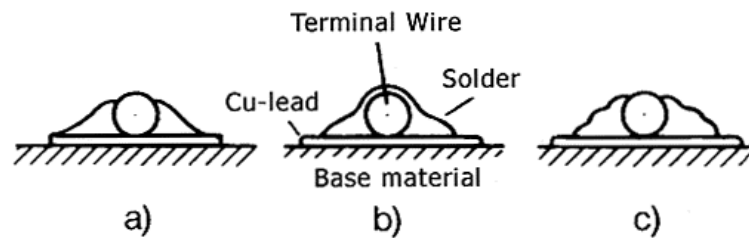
schéma représentant la qualité d'un soudage. (a) fil de fin mal soudé. (b) PCB mal soudé. (c) fil final et PCB mal soudé.
